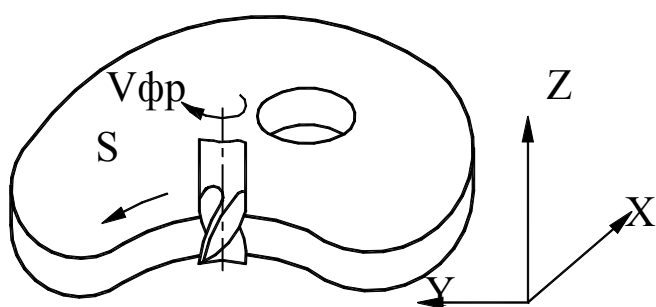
Схема двумерной обработки криволинейной поверхности
